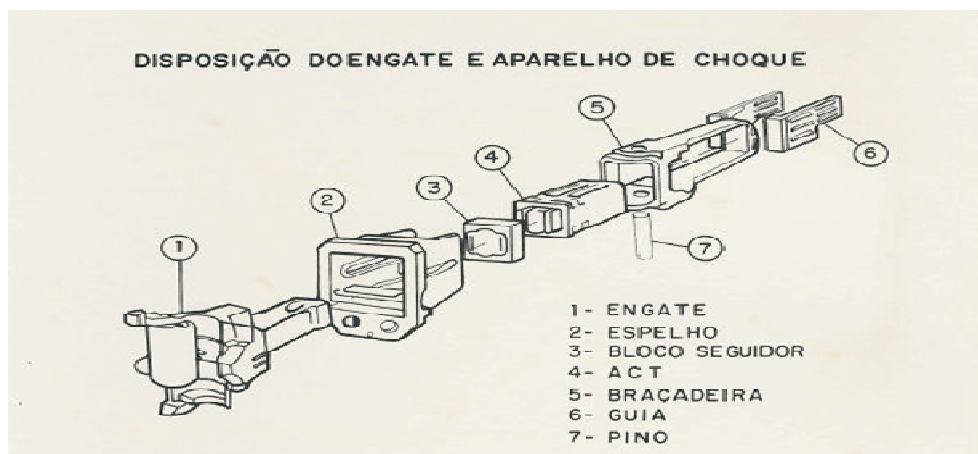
Vista Explodida do Engate e ACT (Fonte: Barbosa, 1993)
